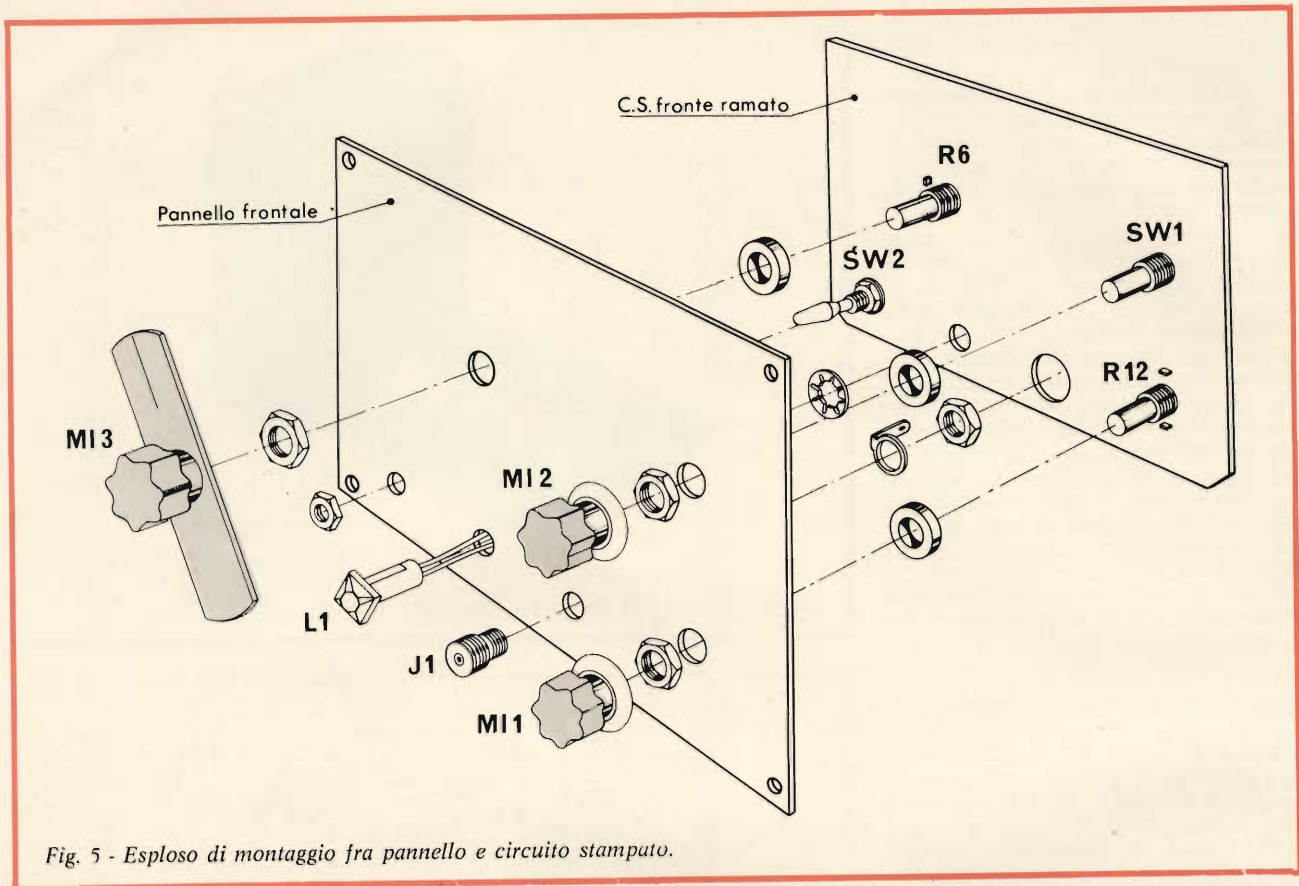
Esploso di montaggio fra pannello e circuito stampato.
